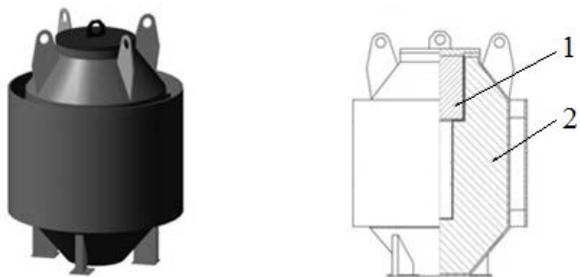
Общий вид контейнера защитного КТИ-160000/4300:
